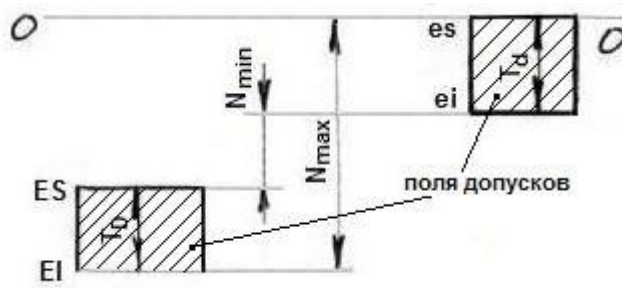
Схема полей допусков для посадки с натягом
